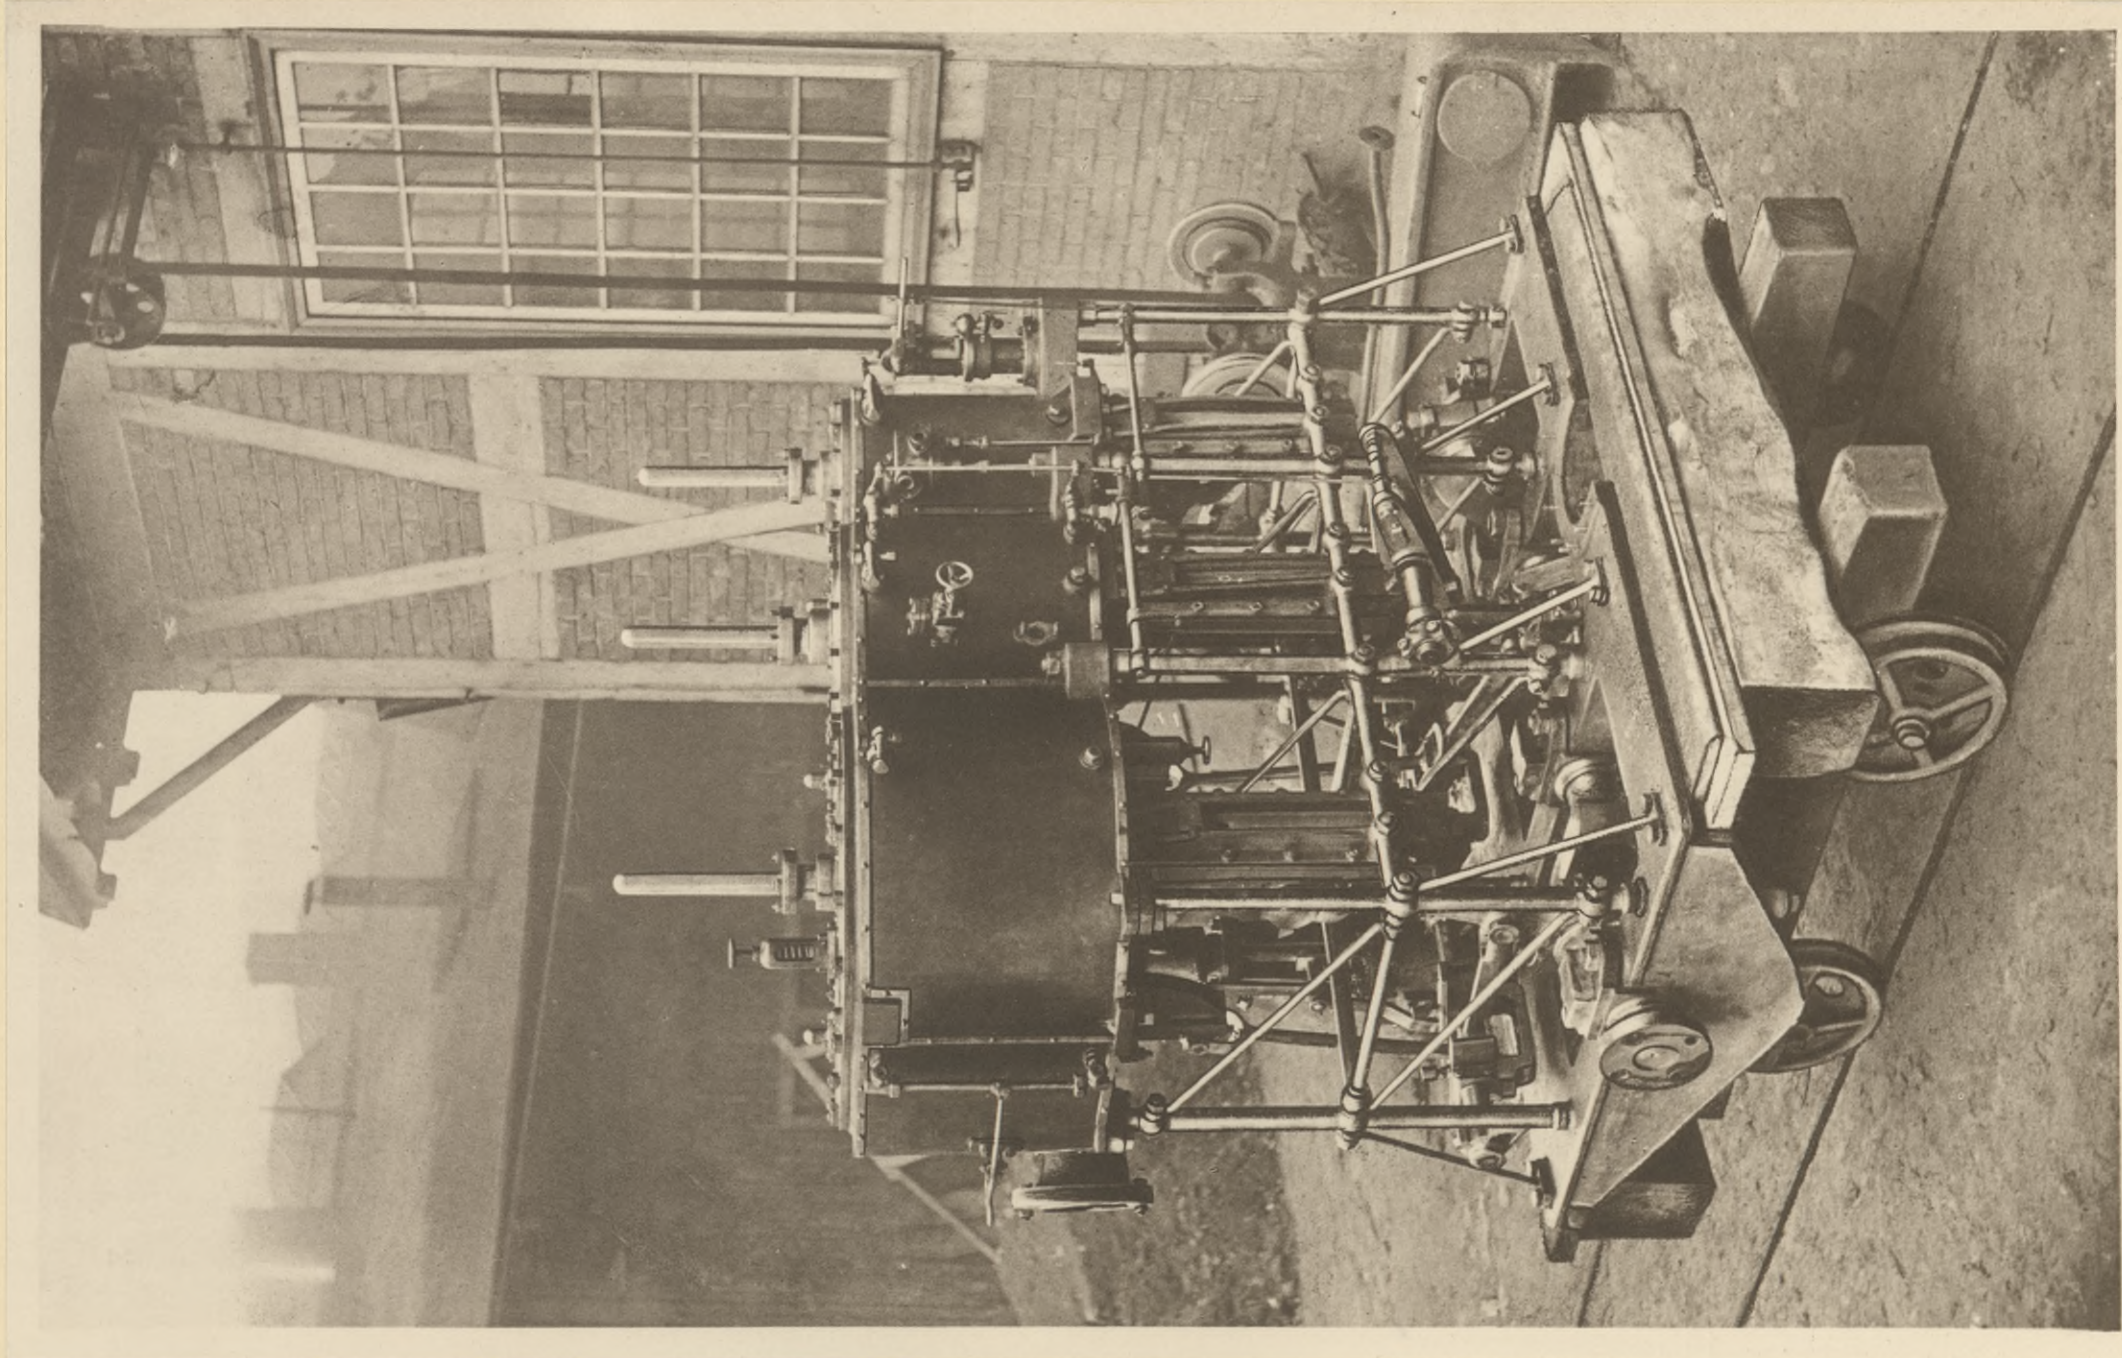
STEUERBORDMASCHINE DES FISCALISCHEN EISBRECHDAMPFERS „SCHWARZWASSER“, 275 indizierte HP.
